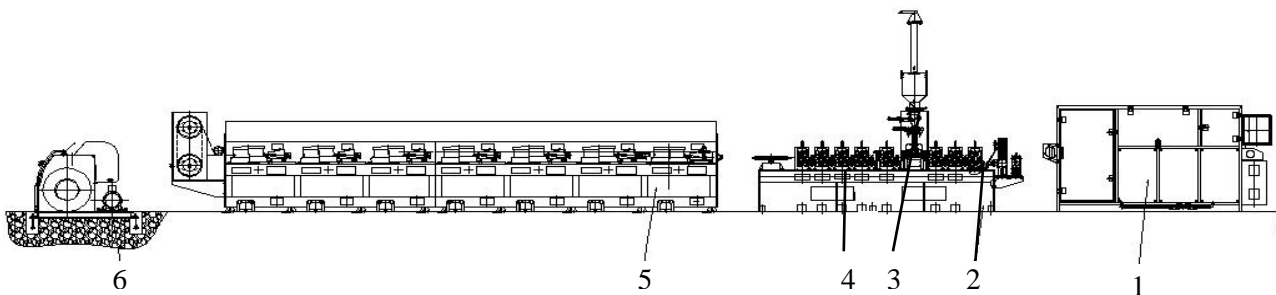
Схема технологічної лінії виготовлення порошкового дроту: 1 - пристрій для очищення сталевих стрічки; 2 - набір формуючих роликів; 3 – дозатор з шихтою; 4 - набір роликів для закриття дроту; 5 – багато барабанний перетягувальний стан; 6 - котушка з готовим дротом.
